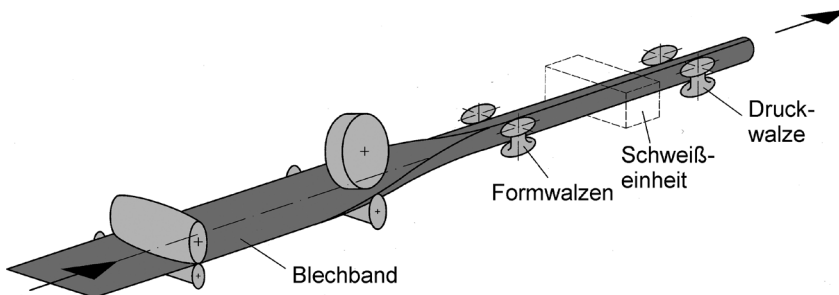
Technologie des Umform- und Fügeprozesses für pressgeschweißte Rohre [43]
